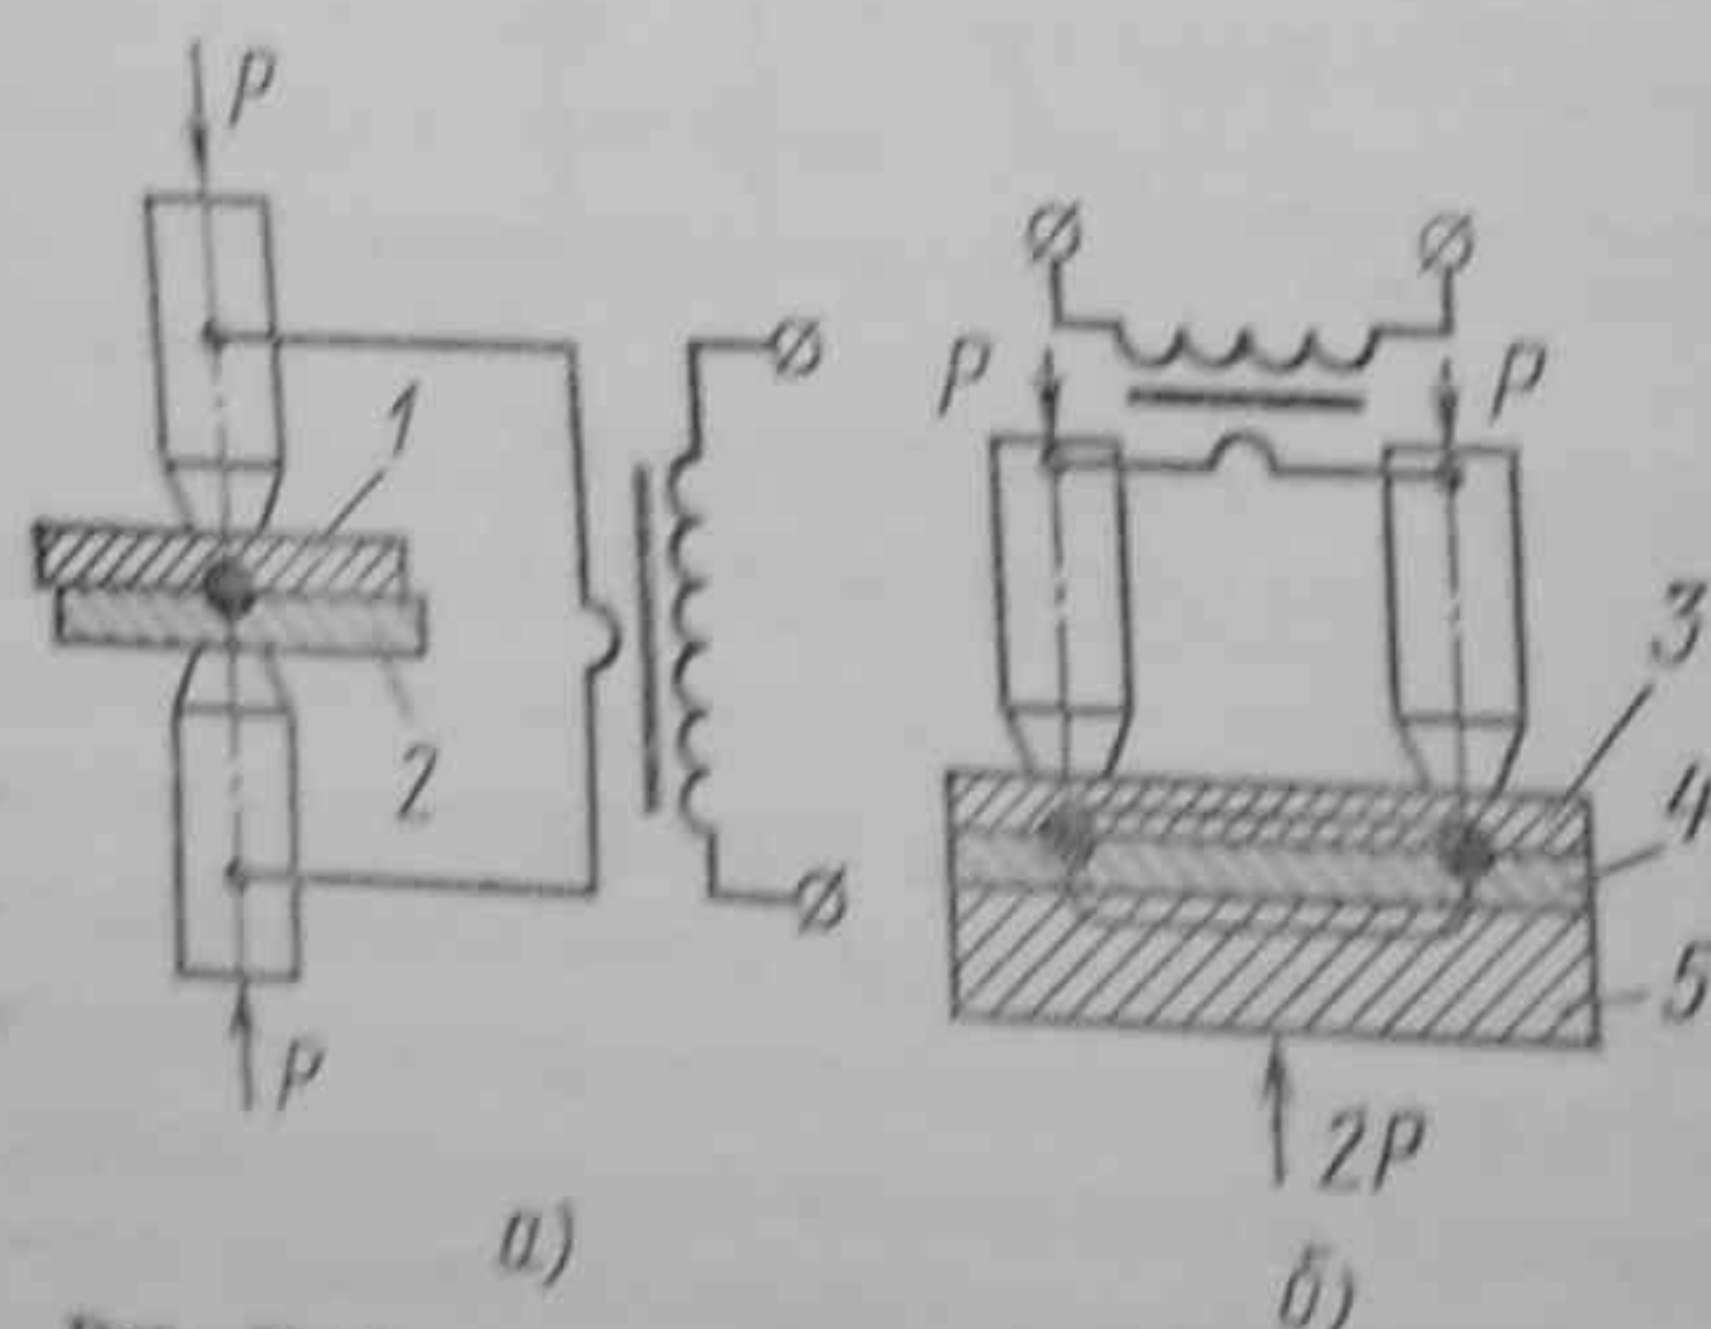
Принципиальная схема контактной точечной сварки:
